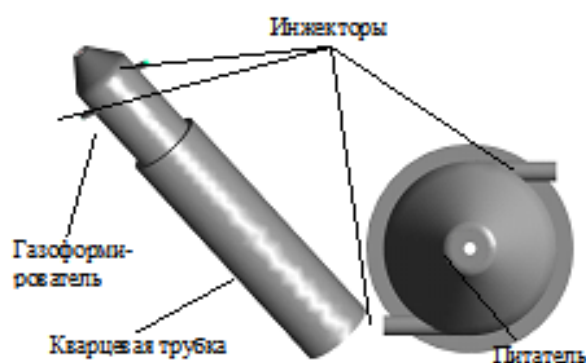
Общий вид и вид сверху разрядной камеры плазмотрона
